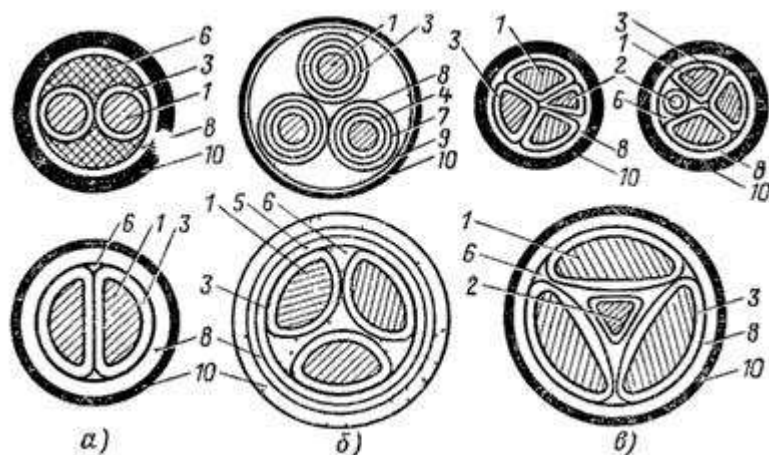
Сечения силовых кабелей: а - двухжильные кабели с круглыми и сегментными жилами, б - трехжильные кабели с поясной изоляцией и отдельными оболочками, в - четырехжильные кабели с нулевой жилой круглой, секторной и треугольной формы, 1 - токопроводящая жила, 2 - нулевая жила, 3 - изоляция жилы, 4 - экран на токопроводящей жиле, 5 - поясная изоляция, 6 - заполнитель, 7 - экран на изоляции жилы, 8 - оболочка, 9 - бронепокров, 10 - наружный защитный покров
